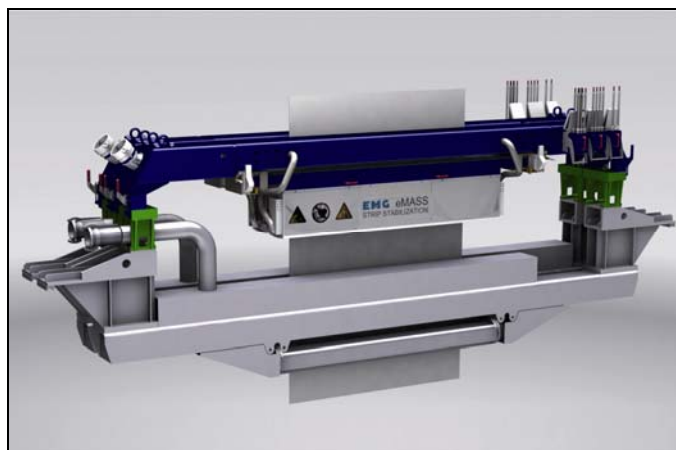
EMG e-MASS: Instalação do equipamento nas facas de ar.
